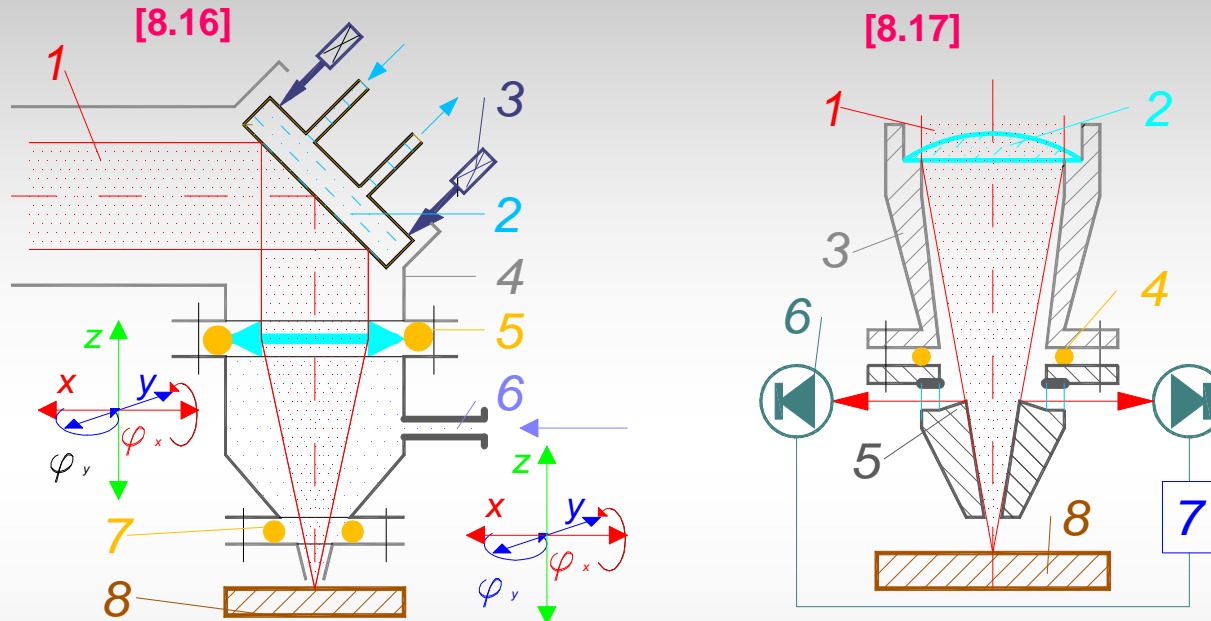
(12.13). Конструкція різаку з додатковими ступенями свободи
